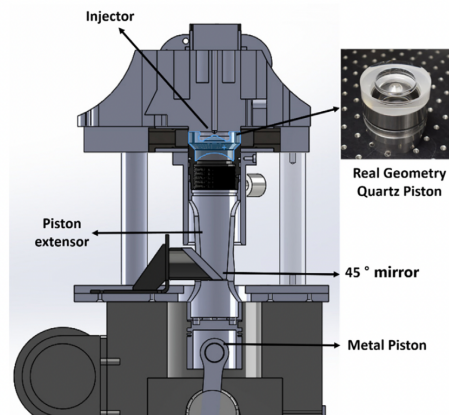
Ejemplo de ensamblaje de un motor óptico diseñado en el CMT [26]
